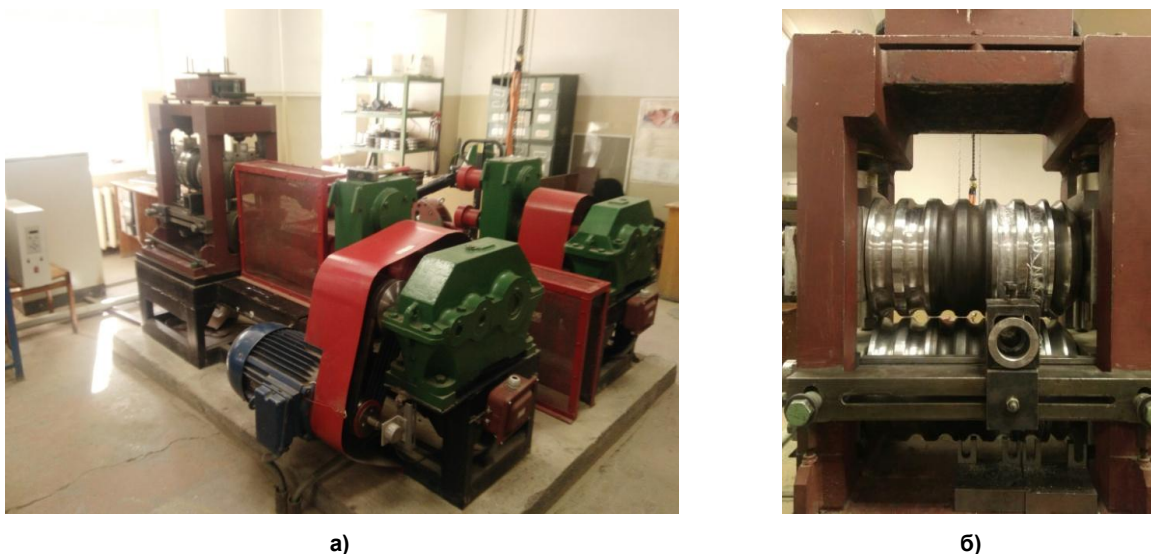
Экспериментальная установка ЭУ-ПППТ: а – общий вид; б – вид со стороны задачи заготовки
